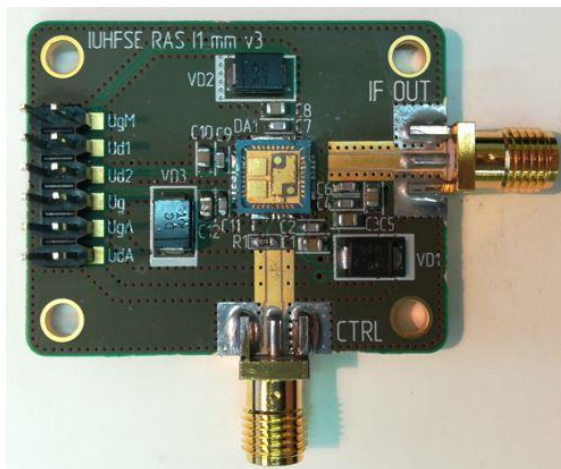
Макет однокристалльного приемопередающего преобразователя сигнала в корпусе без крышки
